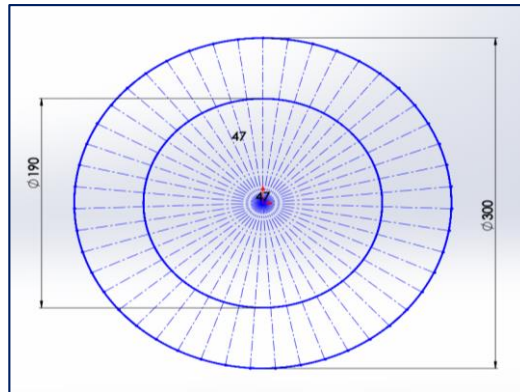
Delineamiento de Ejes Geométricos Principales.
